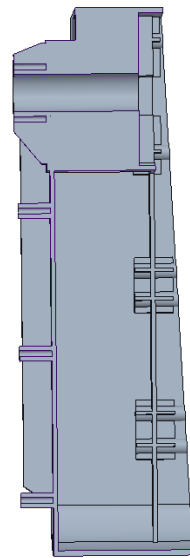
Columna media con los dos planos de atornillado (corte vertical).
